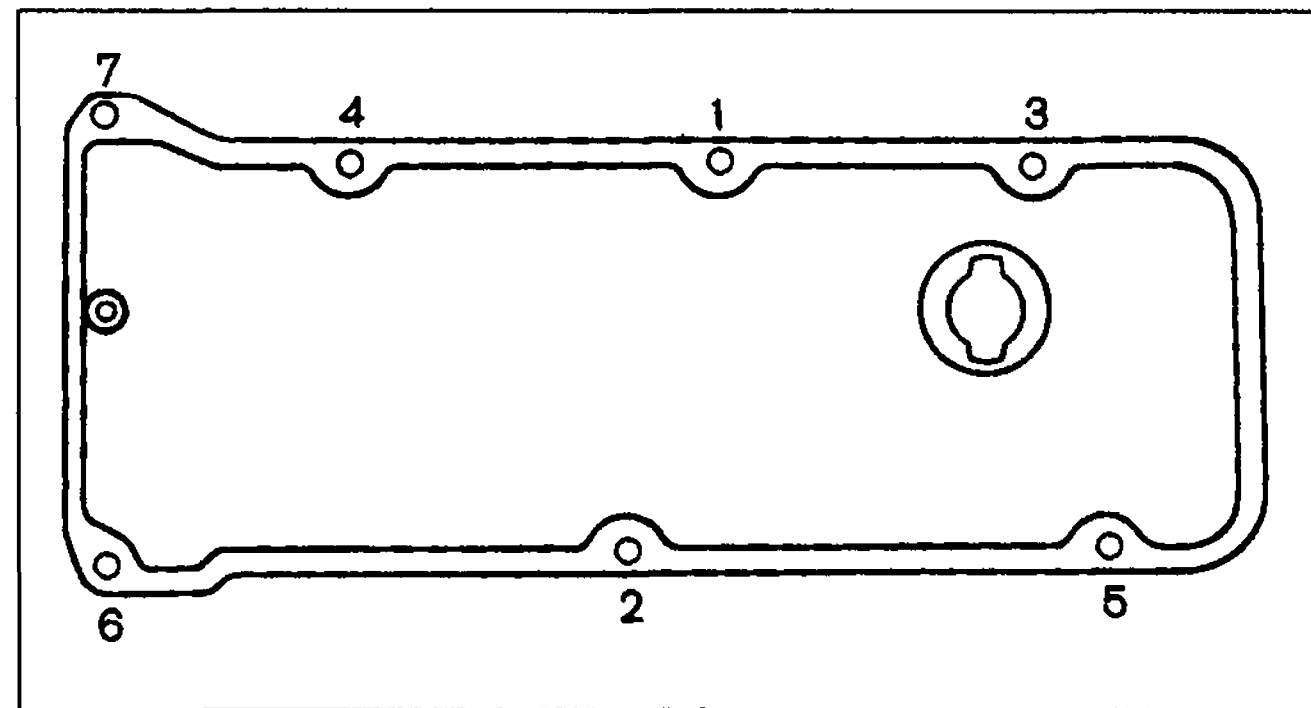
Порядок затягивания гаек крепления крышки головки блока цилиндров
